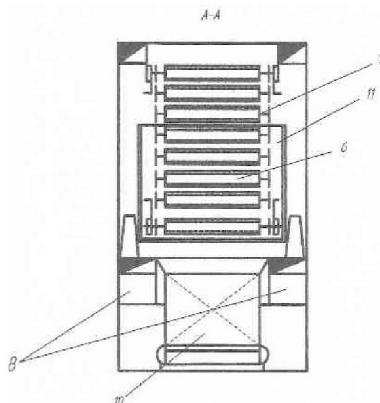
Розріз А-А агрегата для термічної обробки
